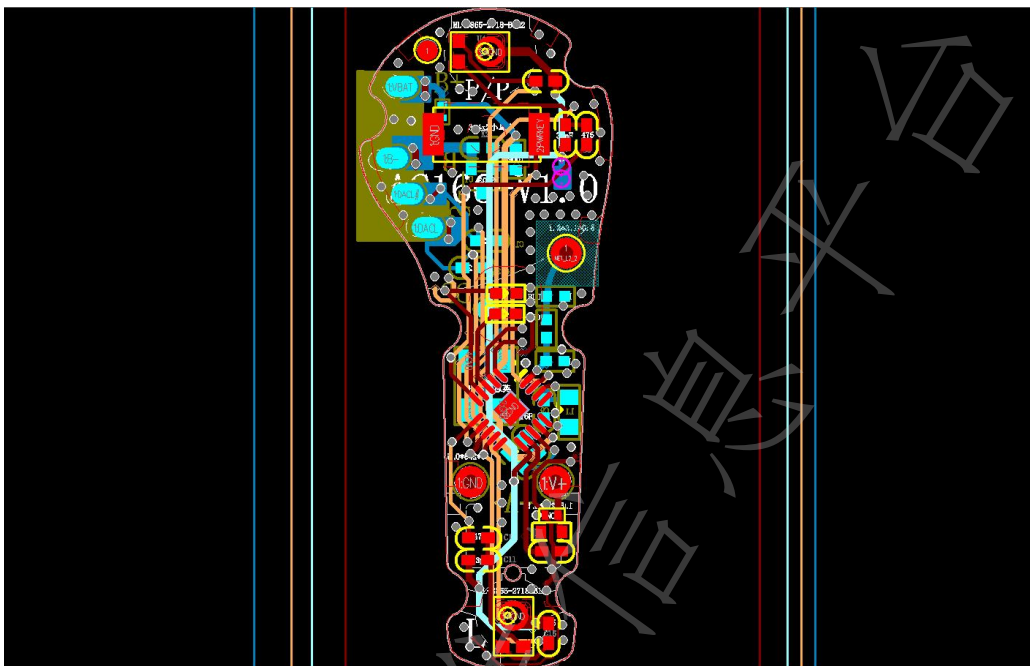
AD02-2002 (AC166) PCB 左耳设计图
